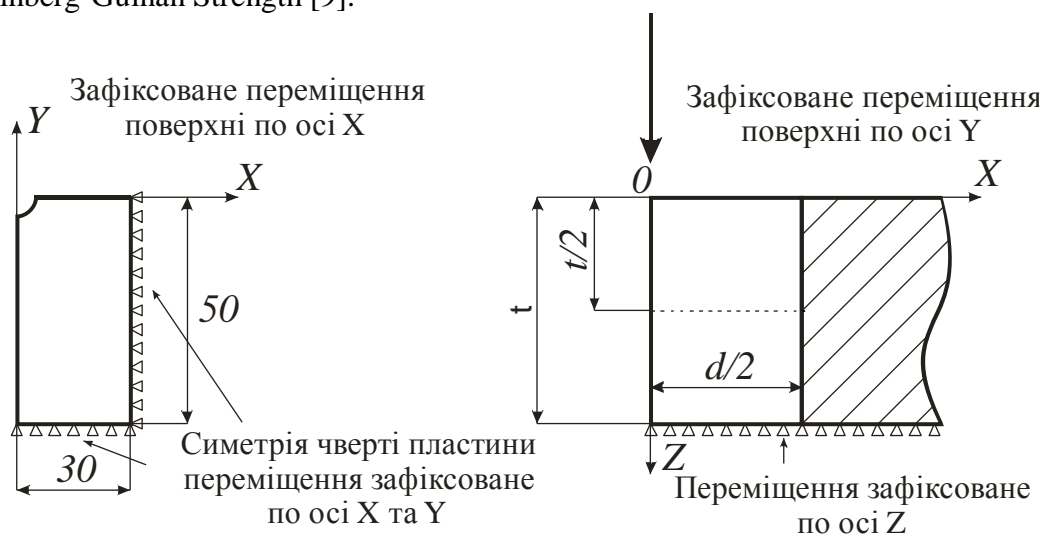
Схема чверті робочої ділянки зразка. Стрілка вказує напрям руху дорна.
